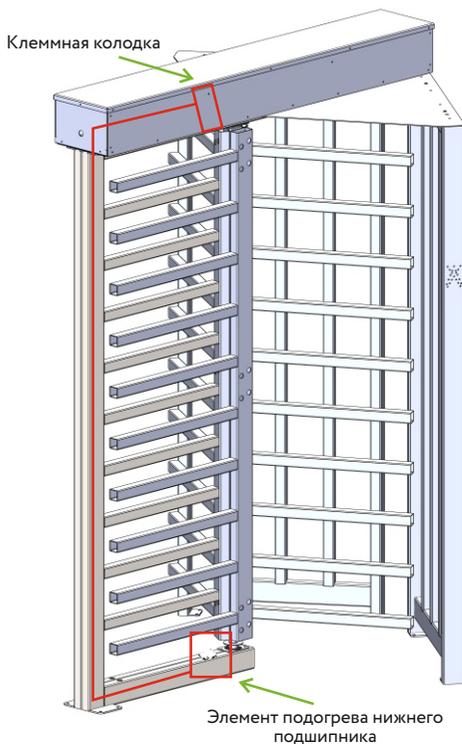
Элементы подогрева в корпусе механизма
